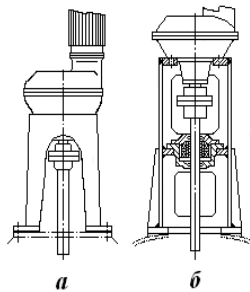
Опорний стаяк ємнісного змішувача:
